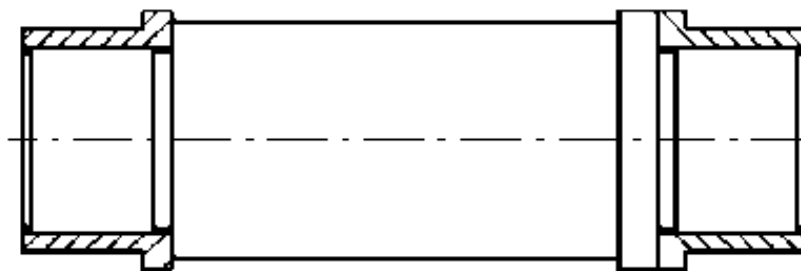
Реализация двойной направляющей базы сочетанием двух цилиндрических поверхностей
